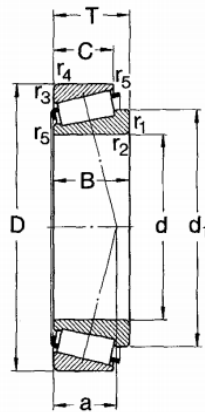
Dimensiones de los rodamientos cónicos de rodillo, skf.
